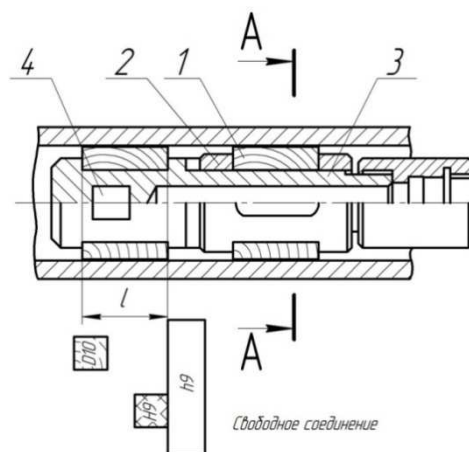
Схема центрирования расточной головки направляющими при свободном соединении с пазами по их длине: 1- направляющая, 2- втулка; 3- корпус борштанги расточного станка; 4 - расточной резец
